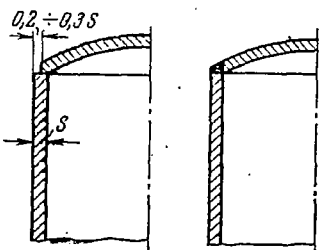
Соединение обечайки с днищем газодуговой сваркой без заточек.
